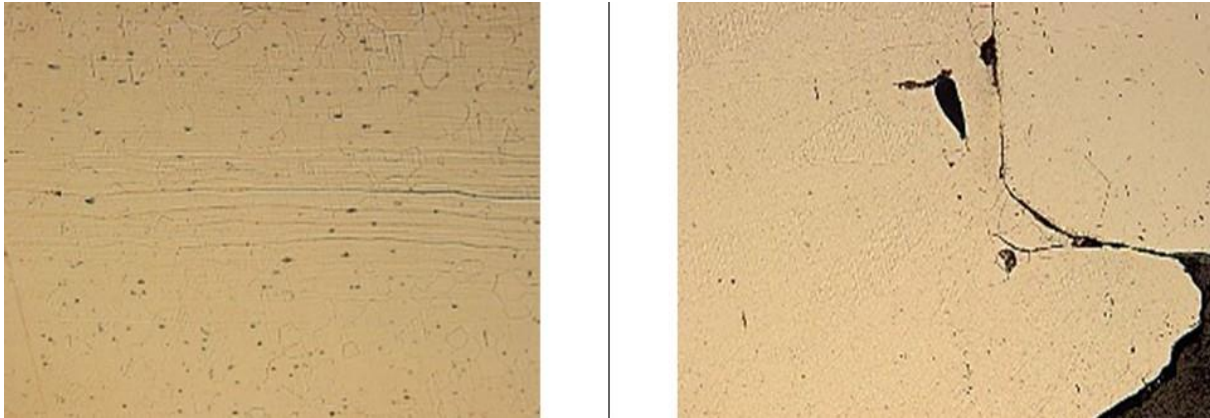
AISI409 1,2 soldagem automática: a) região fora da solda 200x; b) região solda 100x (FONTE: AUTOR, 2017)
